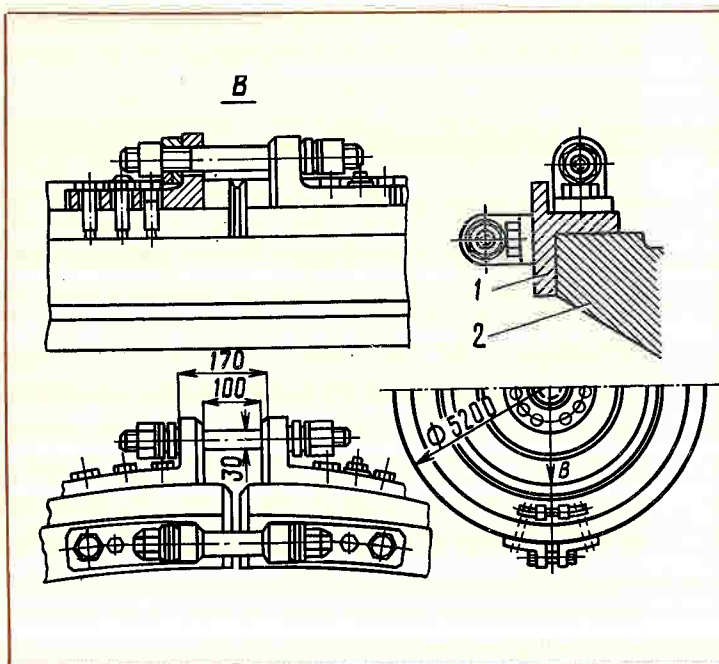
Приспособление для стягивания перед сваркой половинок лабиринтных колец рабочего колеса:
